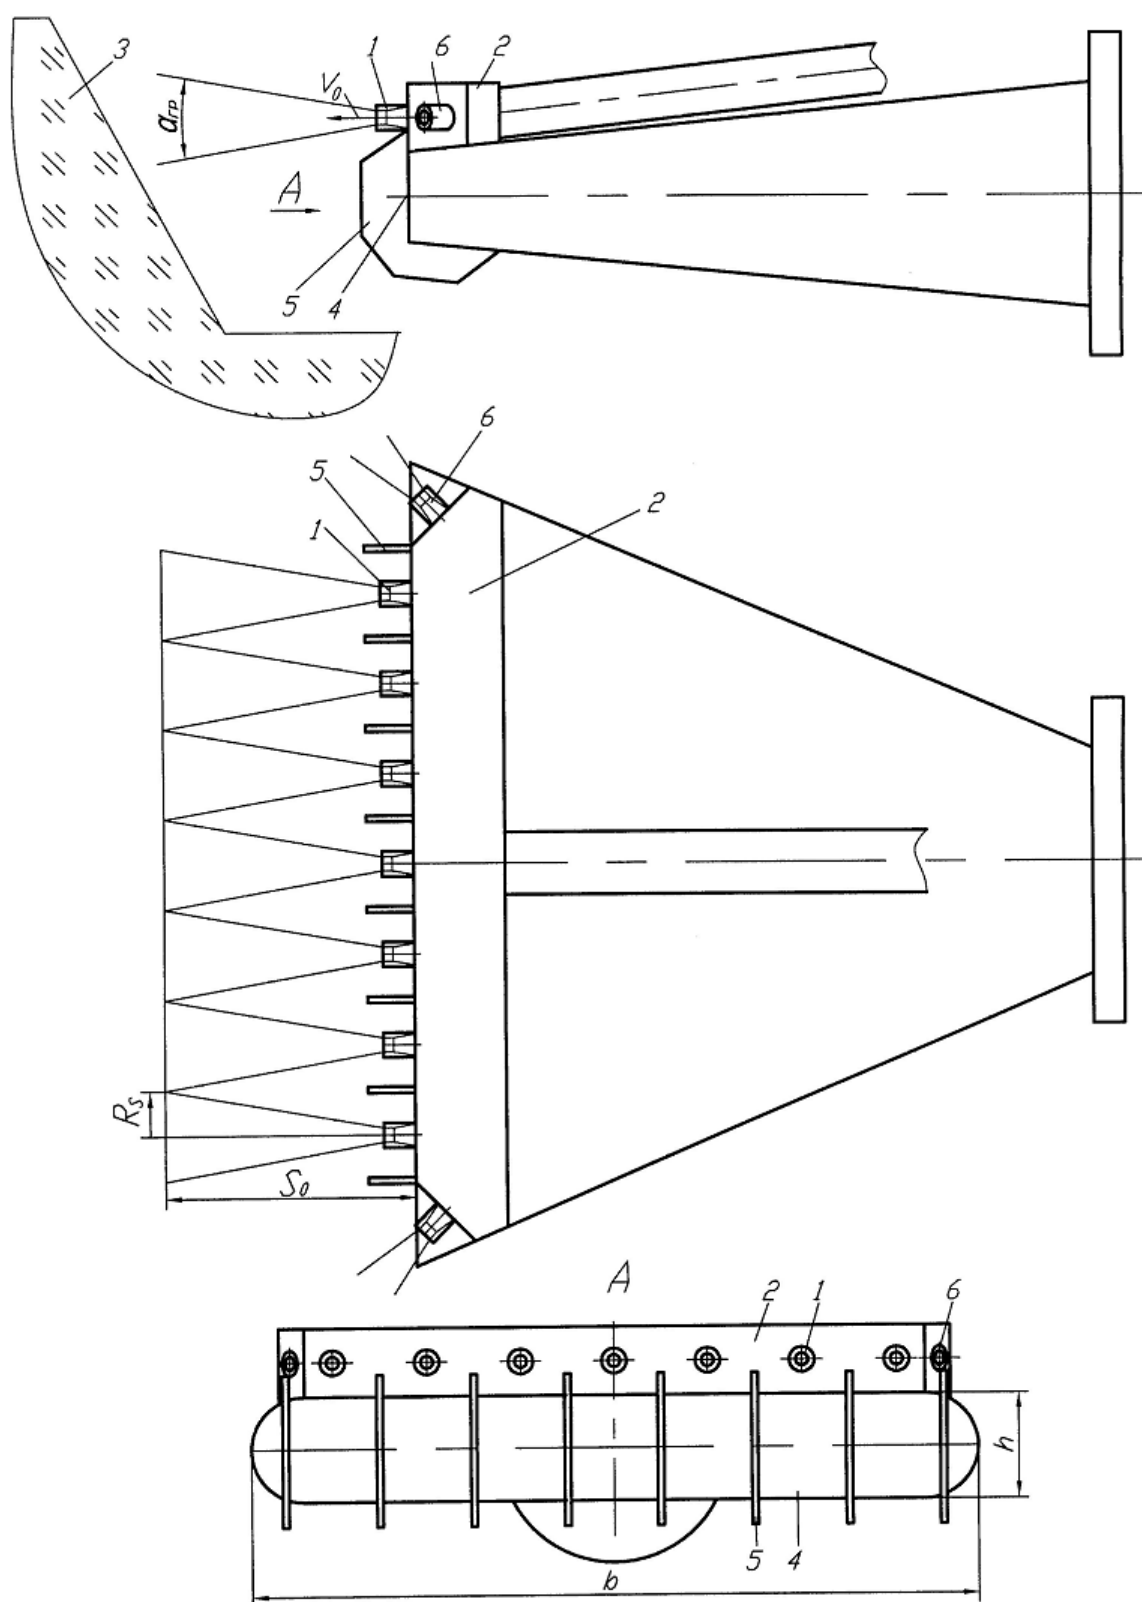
Схема щелевидного грунтоприемника с гидравлическим рыхлителем грунта
